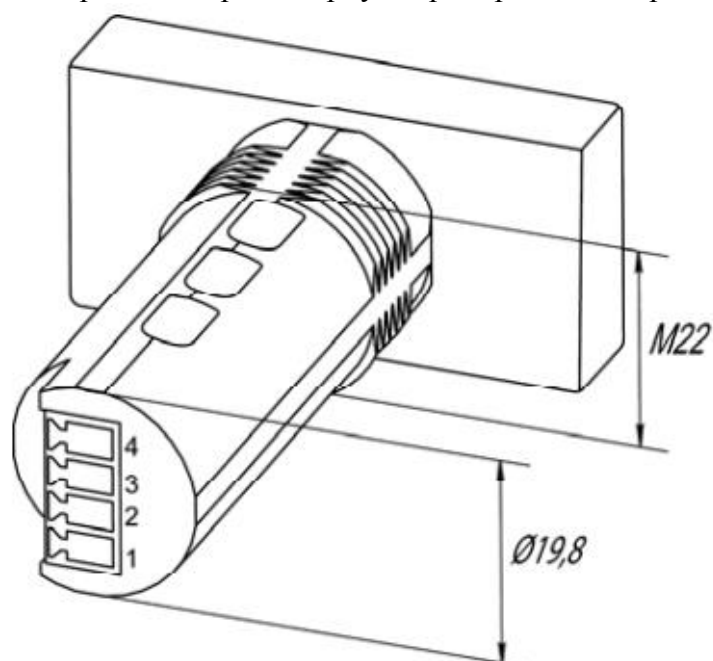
Габаритный чертеж корпуса прибора. Вид сзади.
